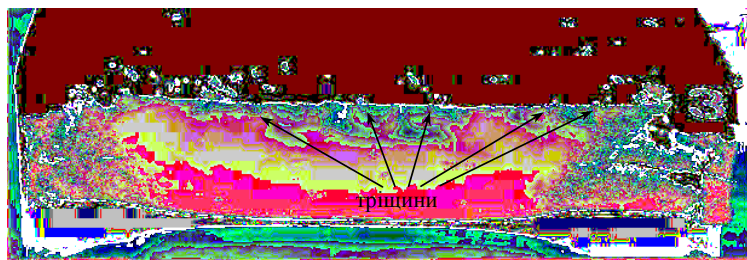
Поверхня руйнування зразка в зоні зварного шва, що демонструє багатоосередковий характер зародження поверхневих тріщин
